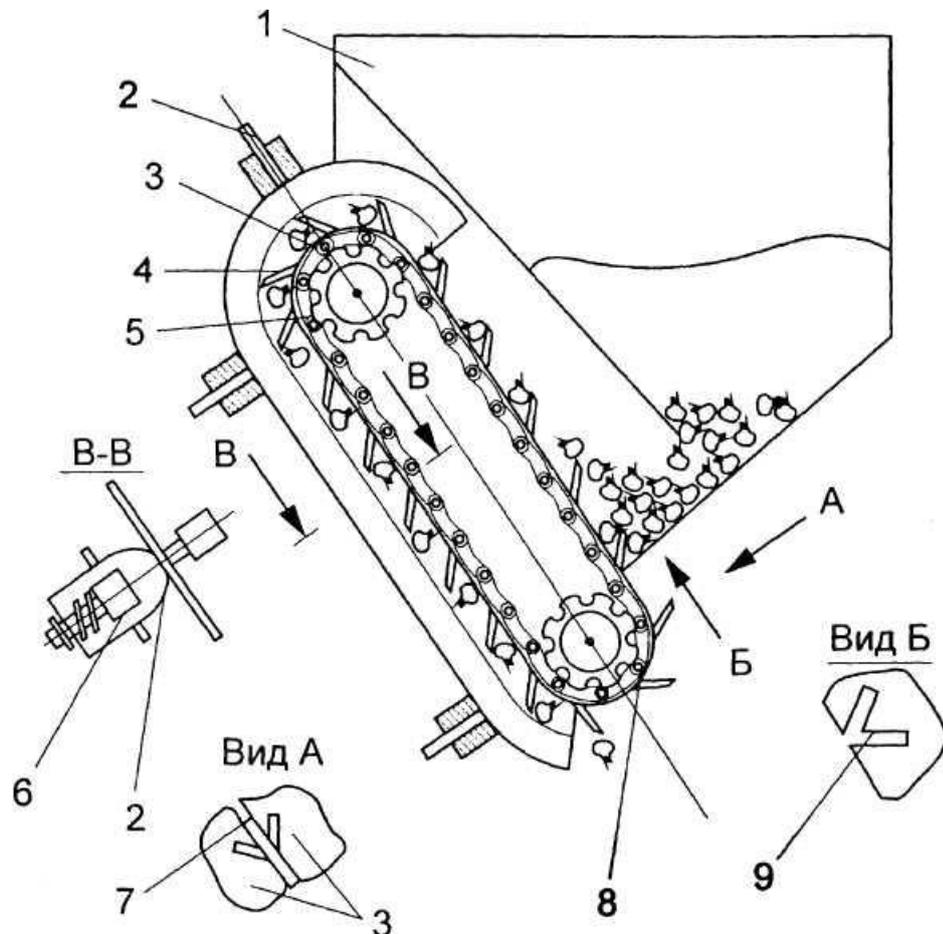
Схема вильчатого высевающего аппарата: 1 – бункер; 2 – цепи транспортера; 3 – кожух; 4 – захват вильчатый; 5 – элемент приводной; 6 – дека; 7 – прорезь; 8 – держатель; 9 – фигурный вырез
